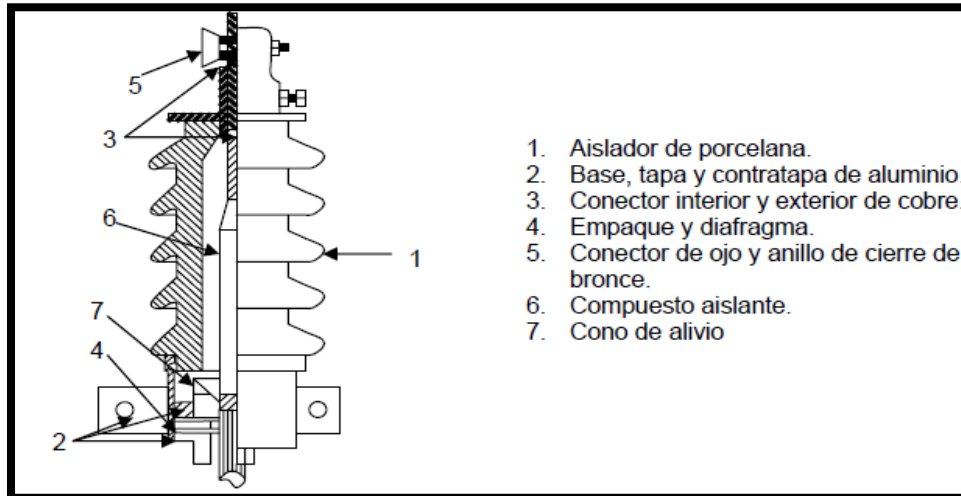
Detalle constructivo de la terminal tipo bayoneta instalada en cable con aislamiento extruido [18].
